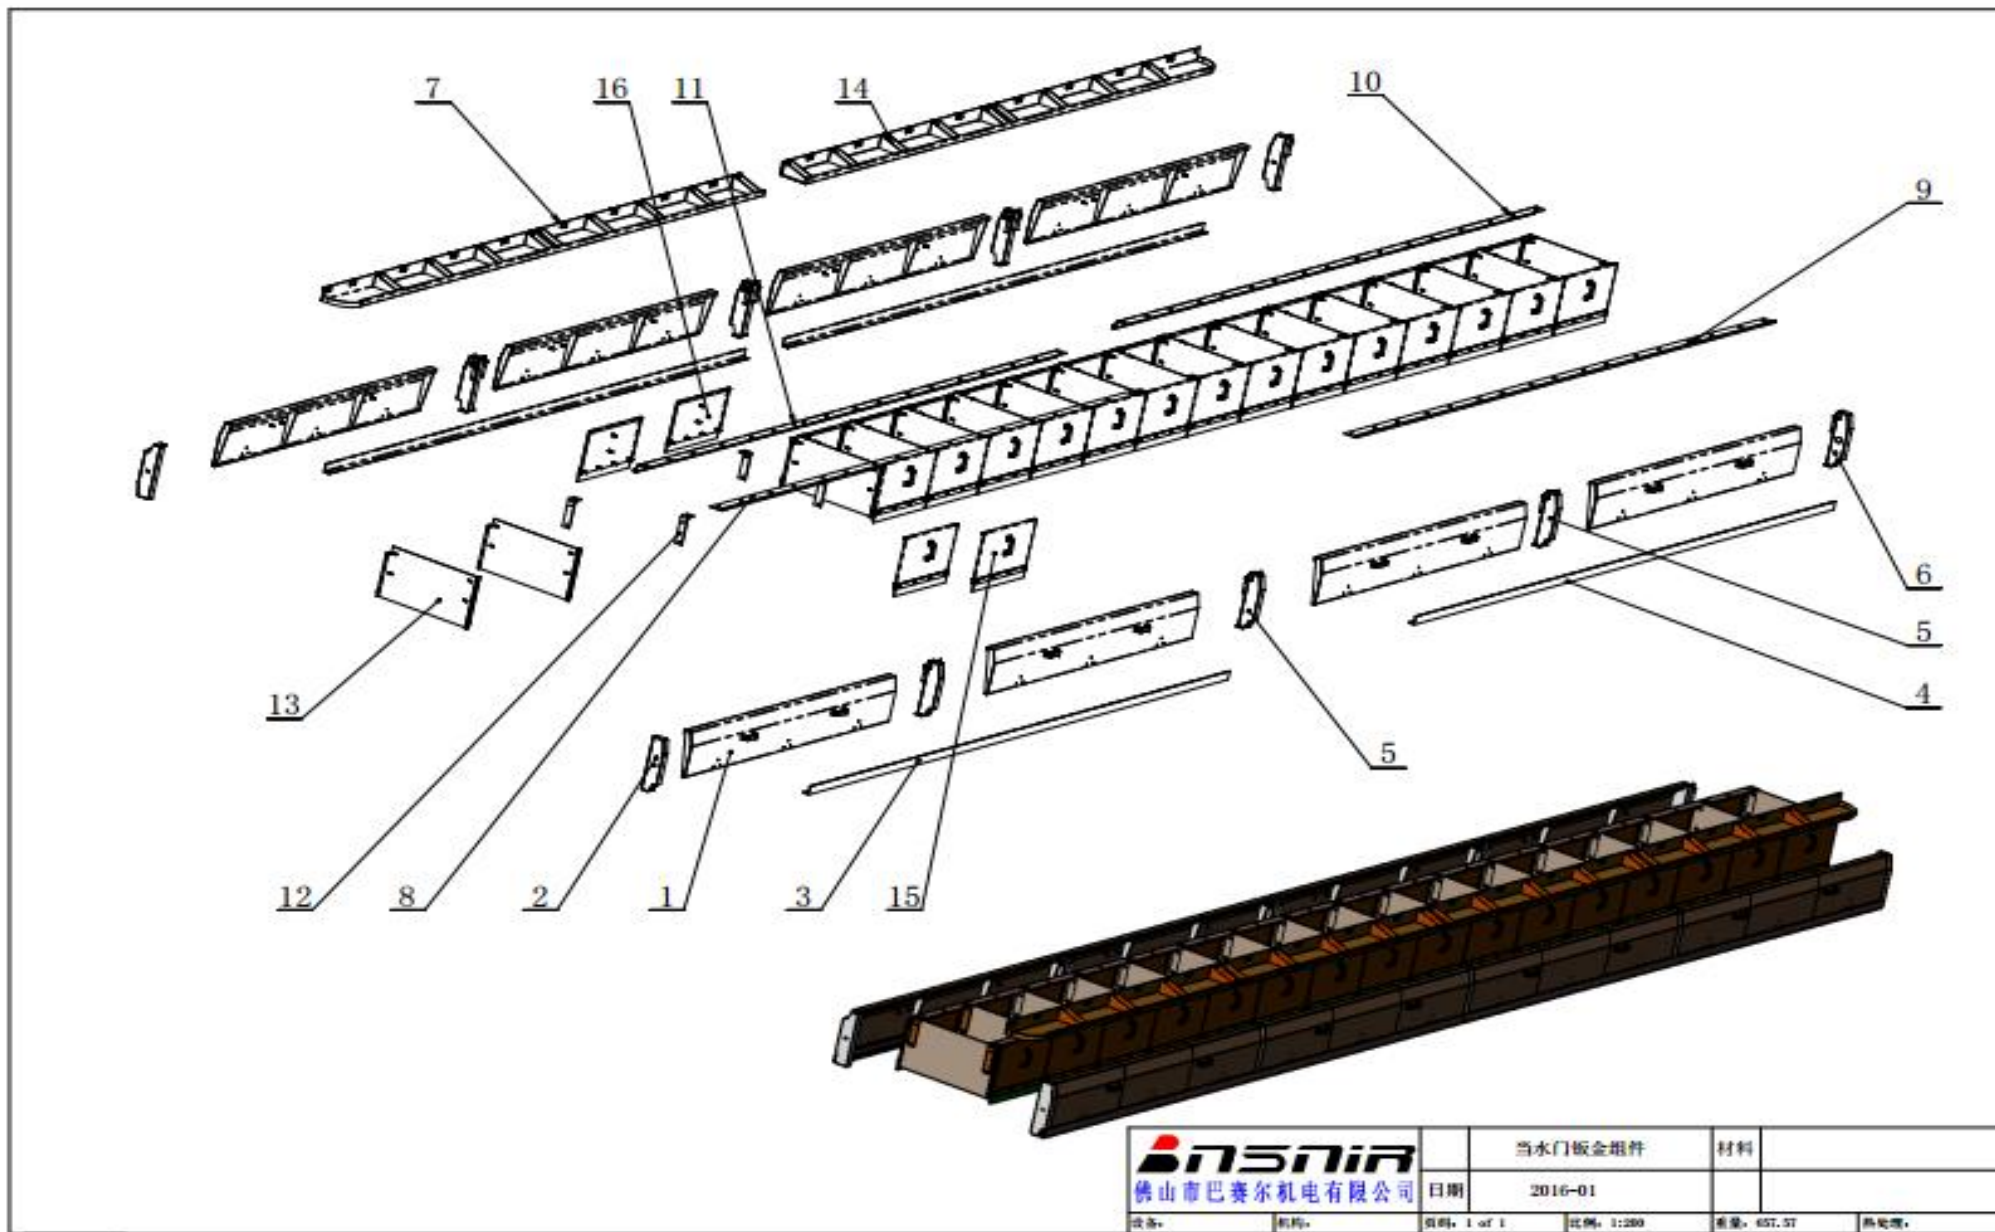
BP1000/16 抛光机 挡水门钣金组件装配图 picture4 Assembly drawing of the sheet metal assembly of the retaining door of BP1000/16 polishing machine
